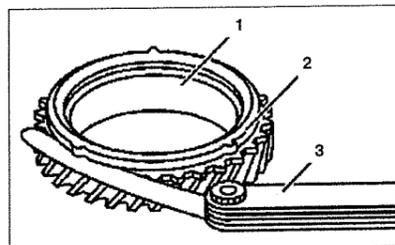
Проверка износа между внутренними кольцами синхронизатора и шестерней 5-й передачи:
